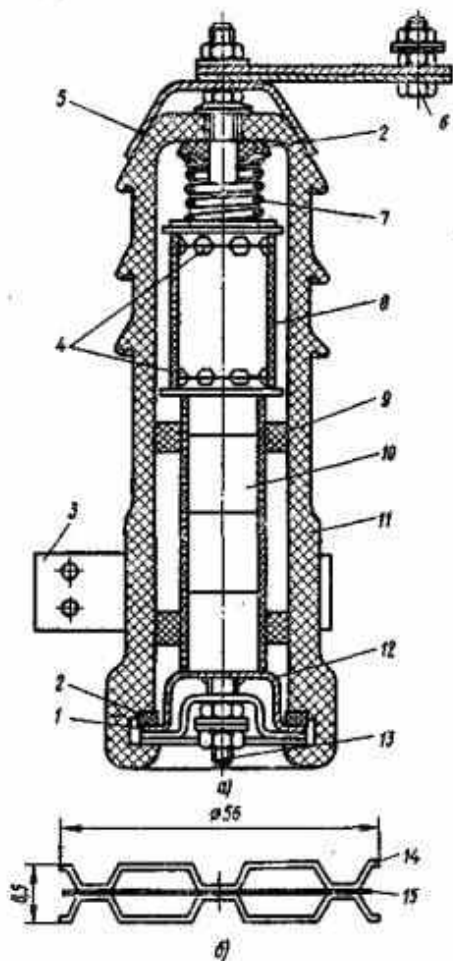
Вентильный разрядник РВП-10: а — общий вид, б — единственный искровой промежуток; 1 — металлический сегмент, 2 — озоностойкая резина, 3 — хомут, 4 — искровые промежутки, 5 — металлический колпак, 6 — болт для присоединения шин, 7 — спиральная пружина, 8 — изоляционный цилиндр, 9 — прокладка из фетра или войлока, 10 — резисторы, 11 — фарфоровый корпус, 12 — нижняя диафрагма, 13 — болт для заземления, 14 — латунный электрод, 15 — изоляционная прокладка из миканита или картона
